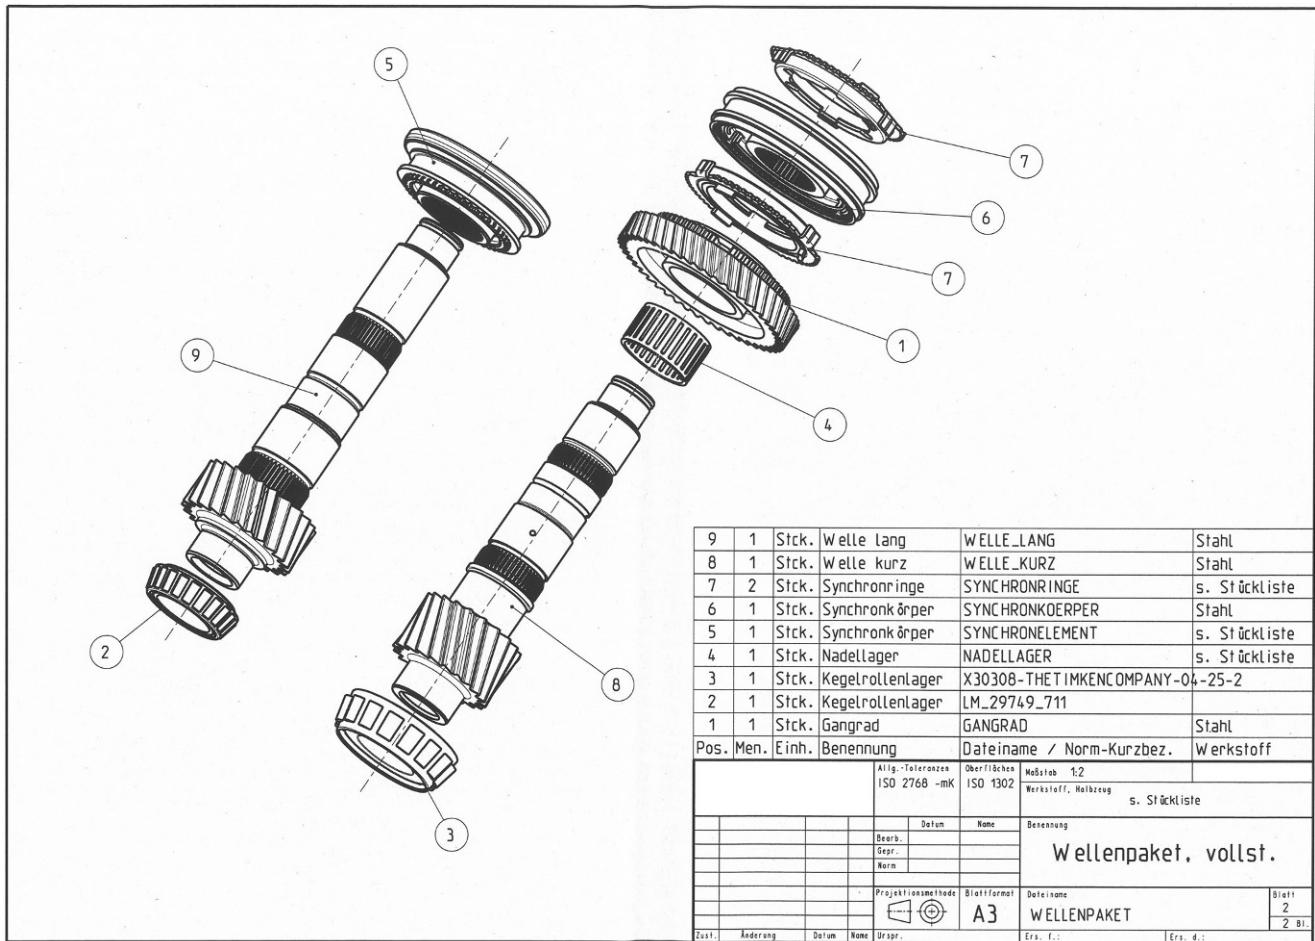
Explosionszeichnung der Wellen 1 und 2
